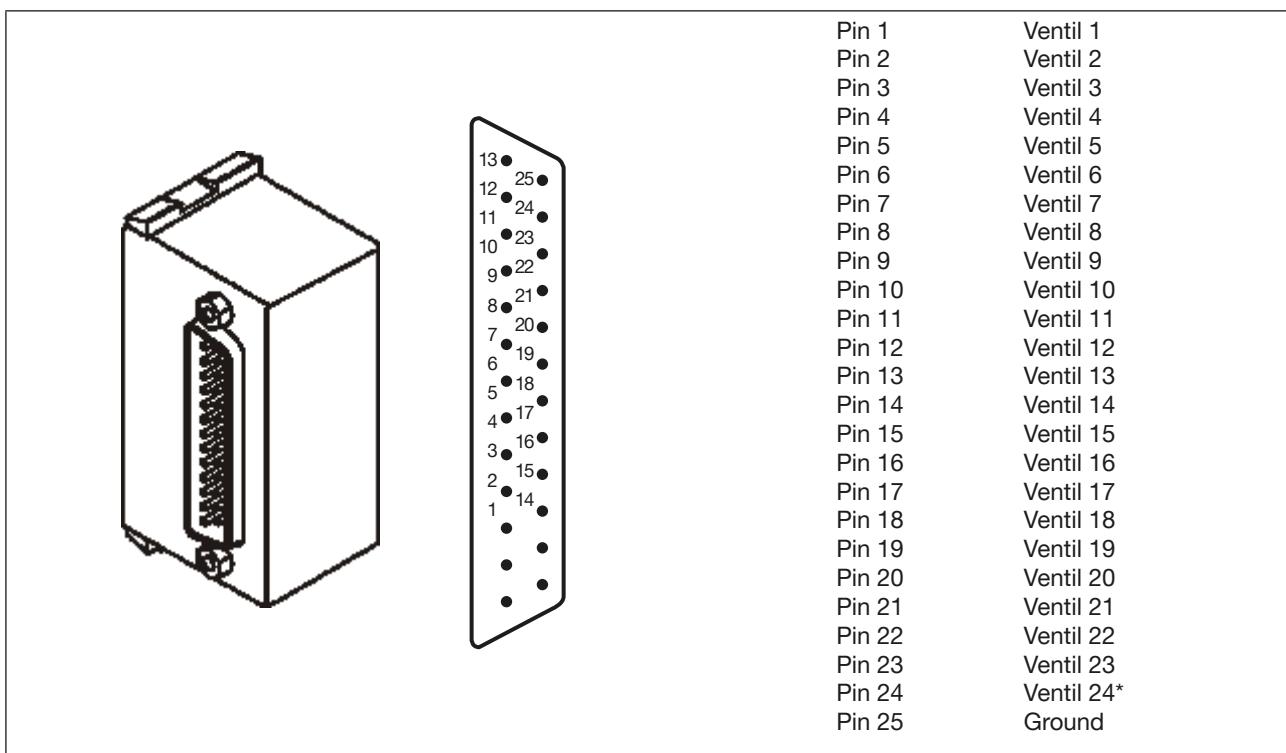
Multipolmodul für Ventilausgänge D-SUB IP54 und Belegung des D-SUB Steckers
